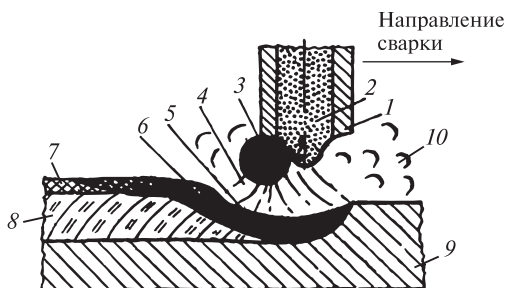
Схема процесса сварки самозащитной порошковой проволокой
